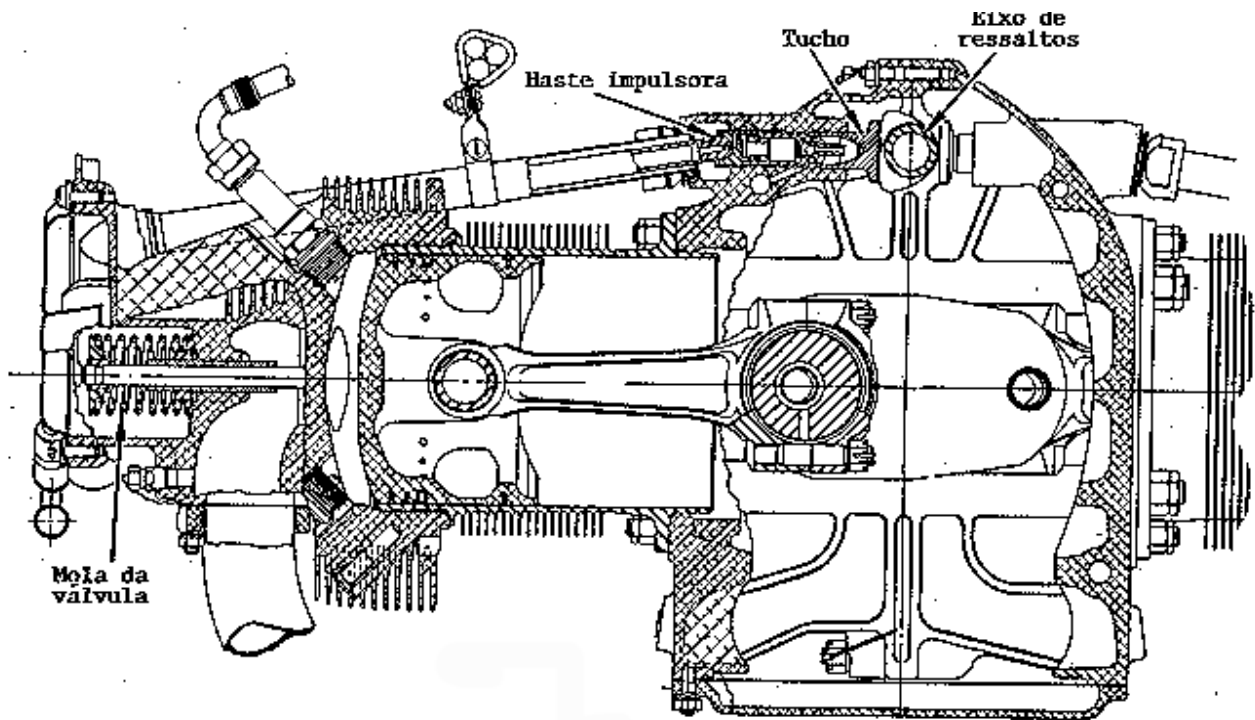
Mecanismo de operação das válvulas (motor de cilindros opostos).
